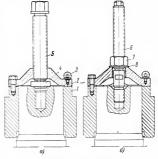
Приспособление для насадки и съема рычагов направляющих лопаток. a — насадка рычагов; b — съем рычагов; b — рычаг; b — корпус; b — рым-болт; b — подкладка; b — внит; b — шпилька; b — гайка: 8 — шайба.
